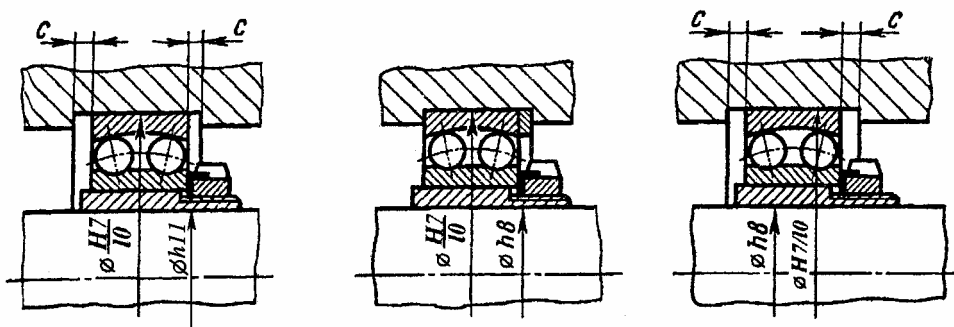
Конструкция вала с плавающими крайними опорами
